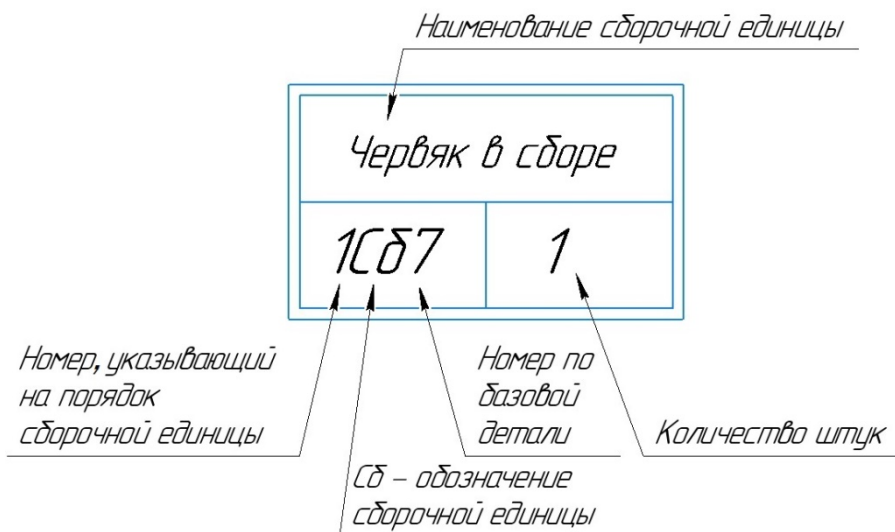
Пример оформления блока сборочной единицы в схеме сборки
